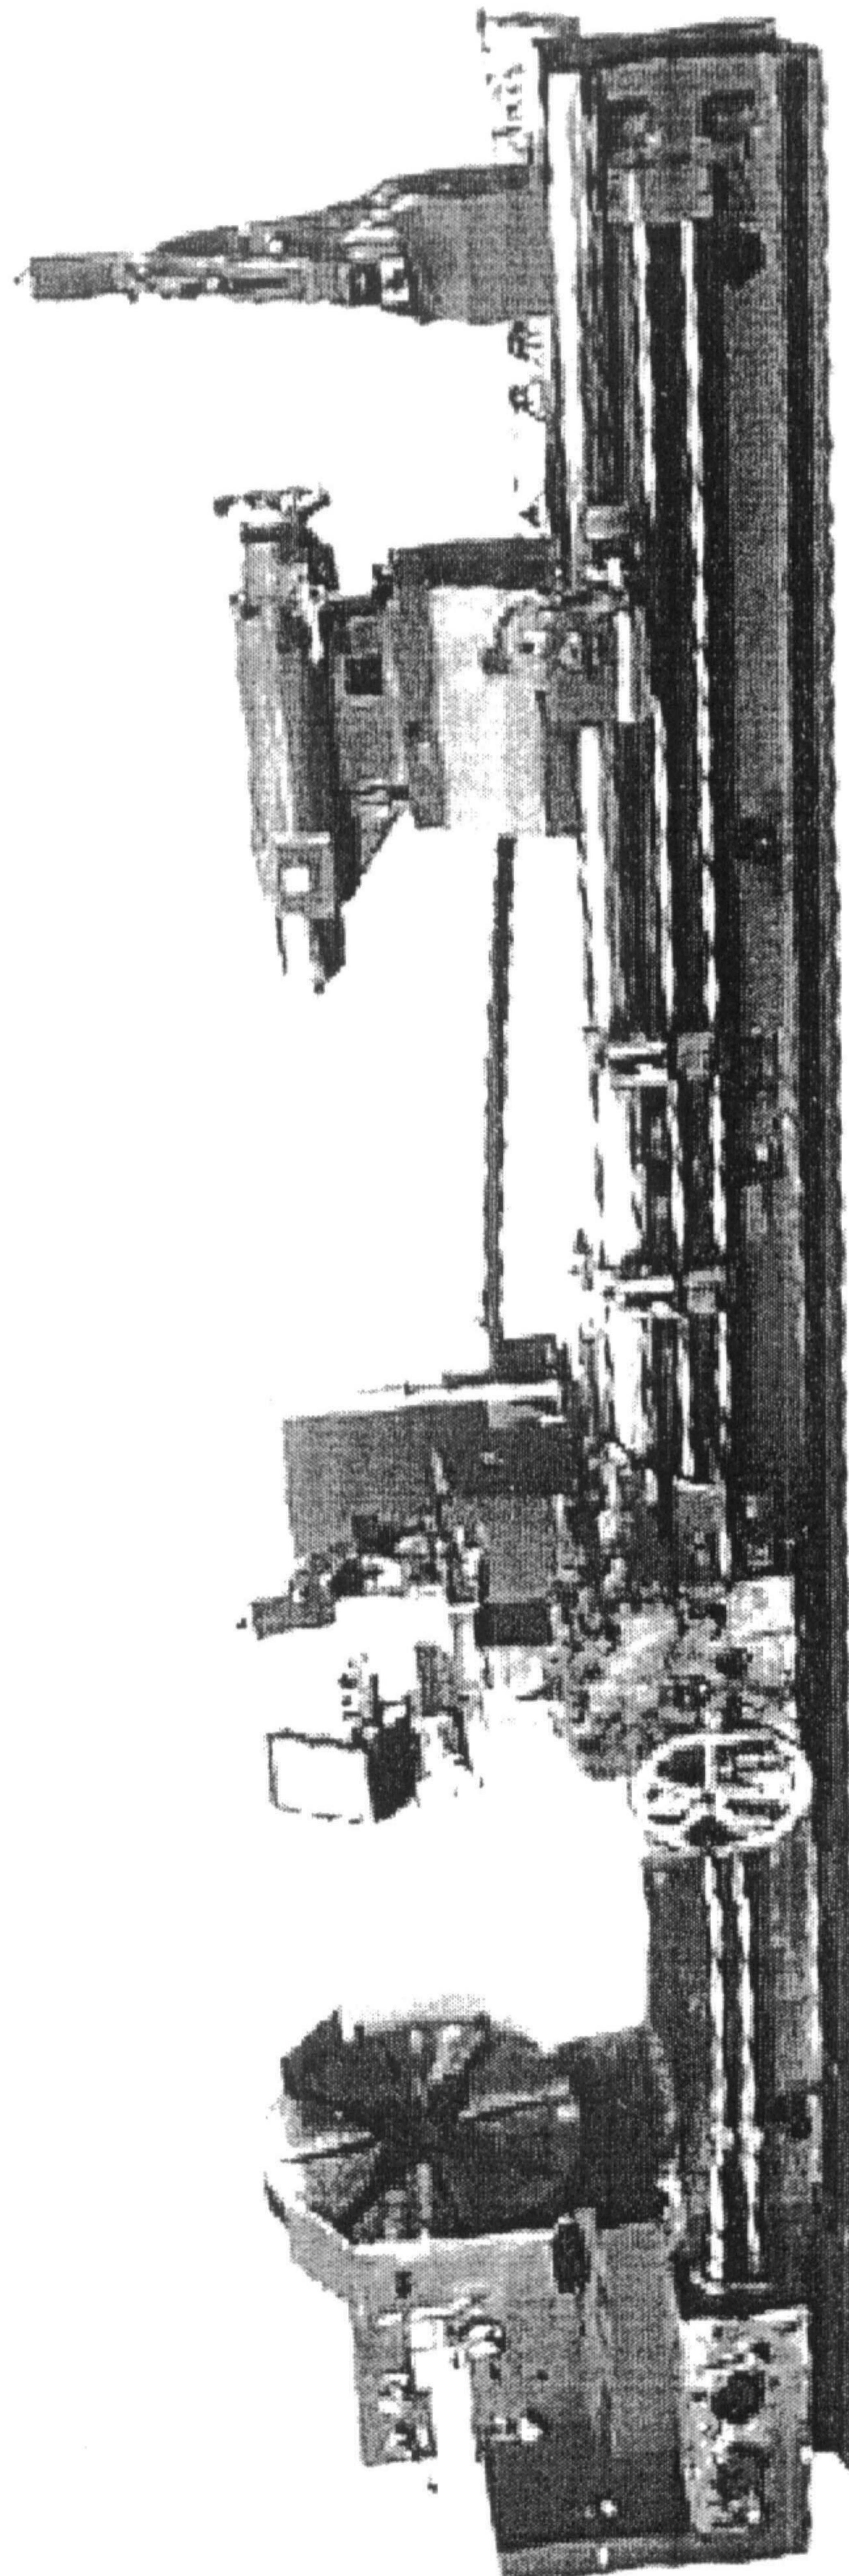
Универсальный токарно-винторезный станок модели 1М65
